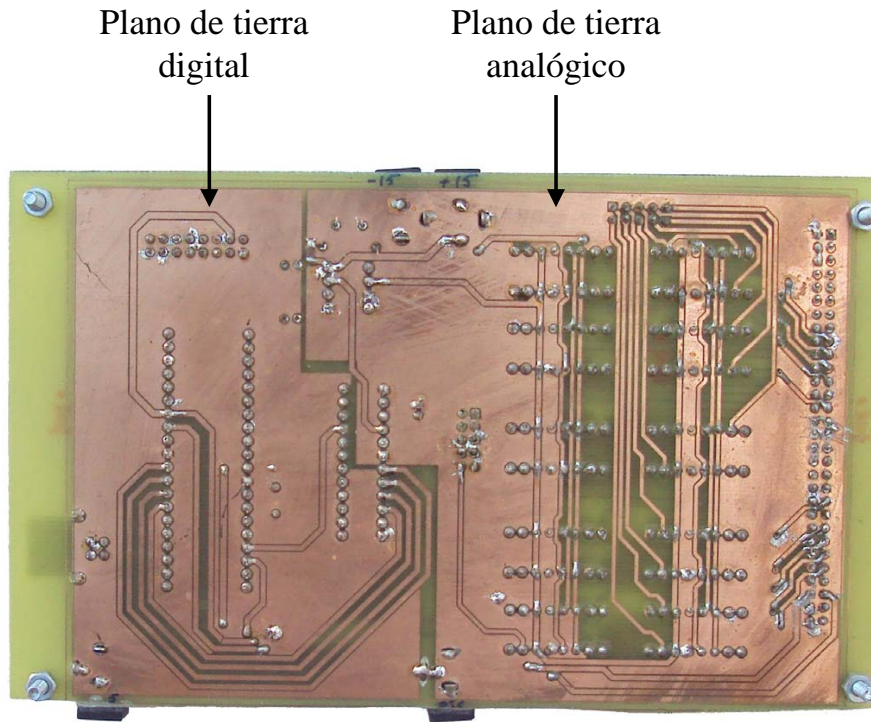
Vista inferior de la PCB del prototipo inicial.
